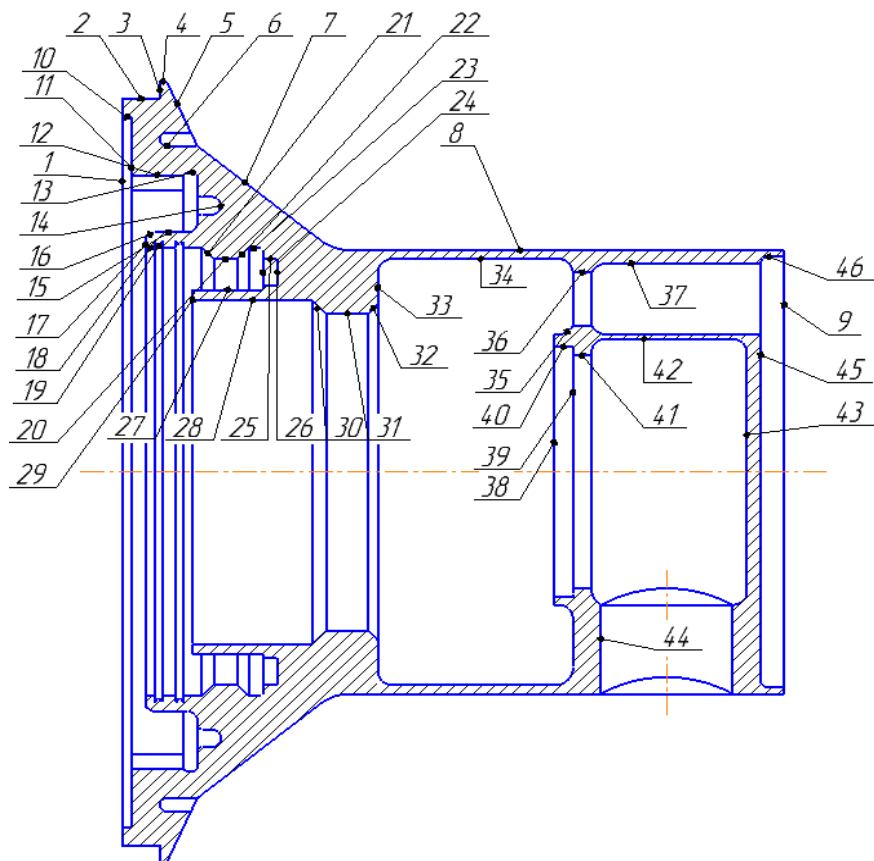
Эскиз детали «Корпус топливно-пусковой системы» с пронумерованными поверхностями
